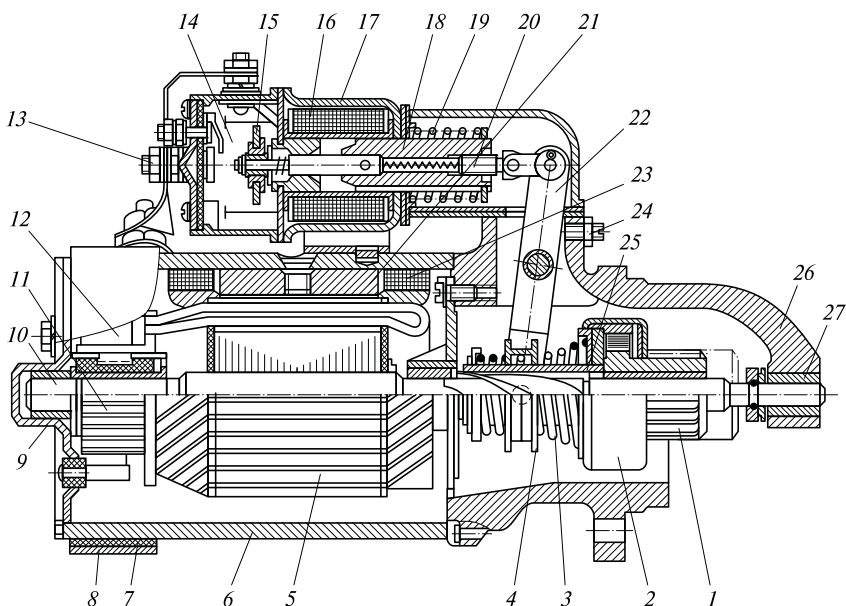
Конструктивная схема стартера с двухобмоточным реле и цилиндрическим коллектором:
